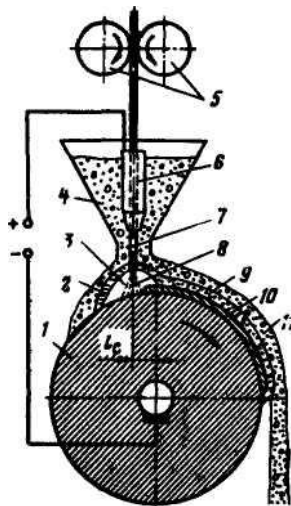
Схема наплавлювальної головки плавки під шаром флюсу: 1 - деталь, що наплавляється; 2 - оболонка з розплавленого флюсу; 3 - газовий простір; 4 - бункер; 5 - ролики подачі дроту; 6 - направляючий мундштук; 7 -
